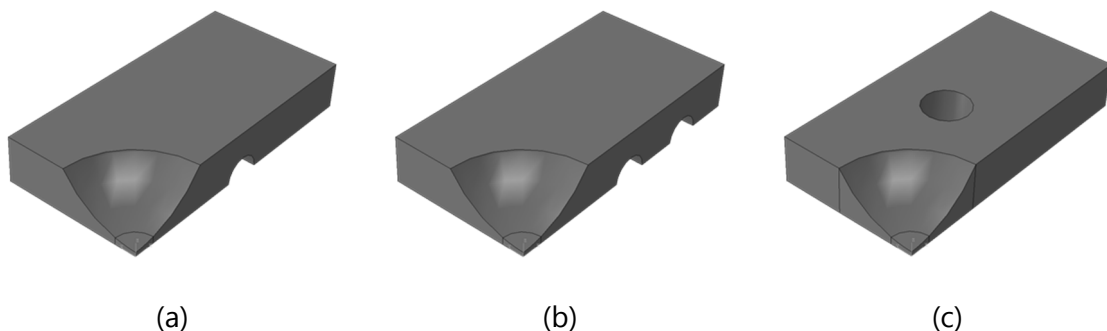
Quaderförmige Proben mit rechteckiger Grundfläche und halbkugelförmiger Einziehung, sog. „Kalottenproben“ (3D-Achtelmodelle) (a) kurze horizontale Kühlbohrung; (b) zwei kurze horizontale Kühlbohrungen; (c) axiale Bohrung.
